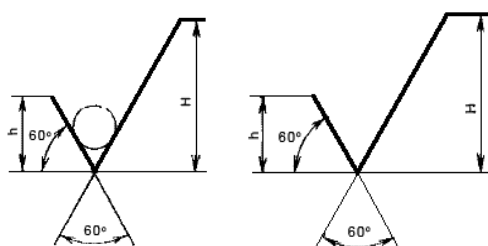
Знаки условного обозначения шероховатости поверхности
